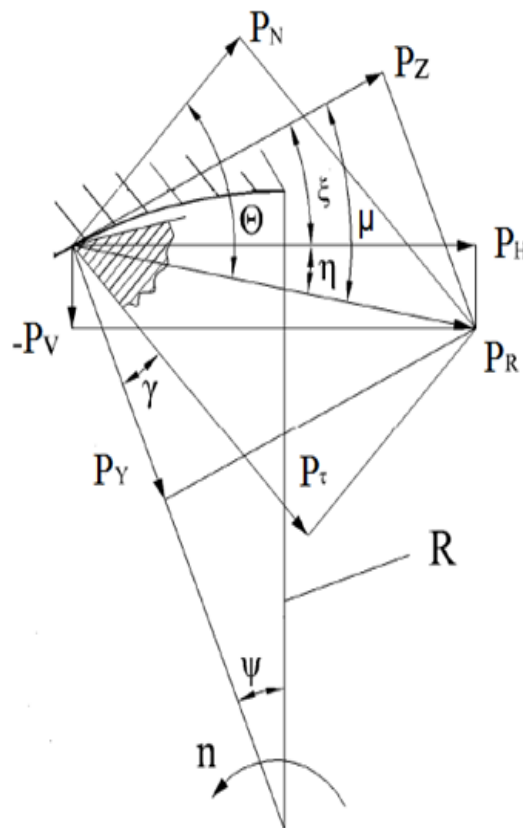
Силы, действующие на зуб концевой фрезы в модели встречного фрезерования.
